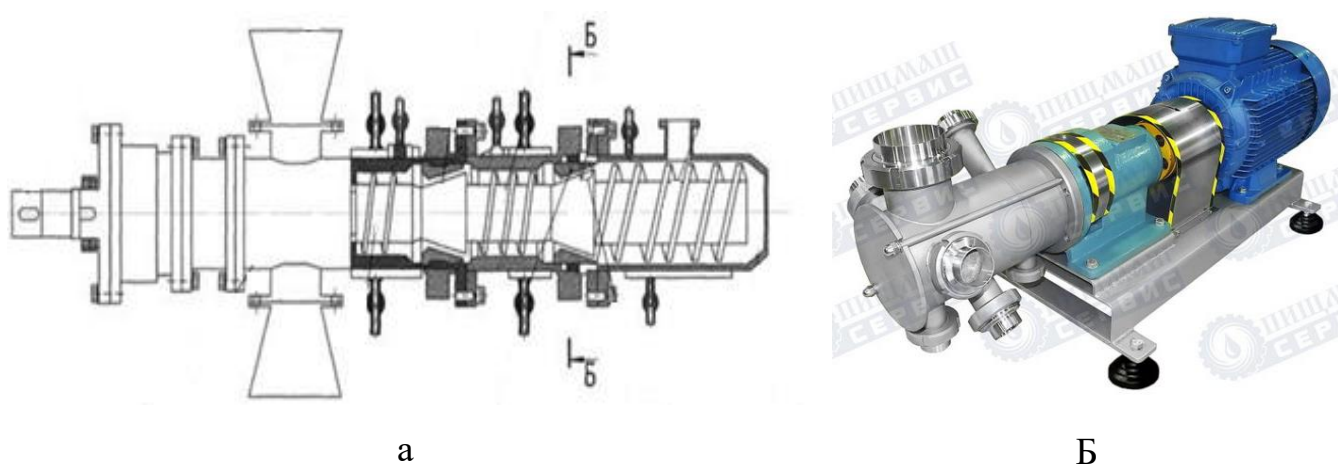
Схематичне зображення (а) і загальний вигляд (б) гвинтового диспергатора [92]
